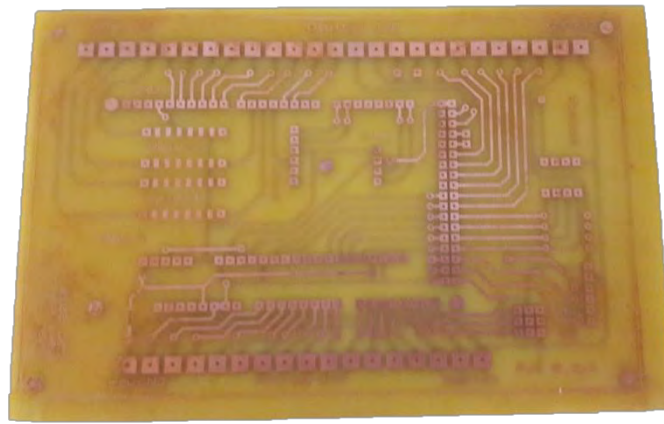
Placa de FR4 impresa, previa al proceso de soldadura de componentes.
